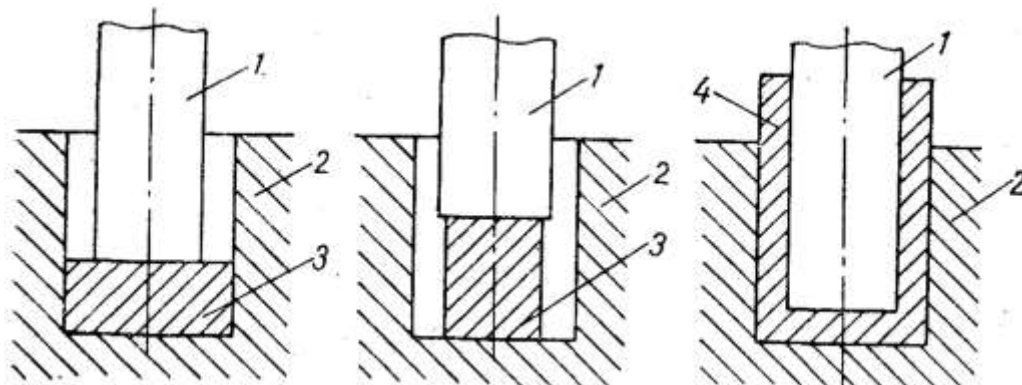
Схеми штампування поковок прошиванням:
